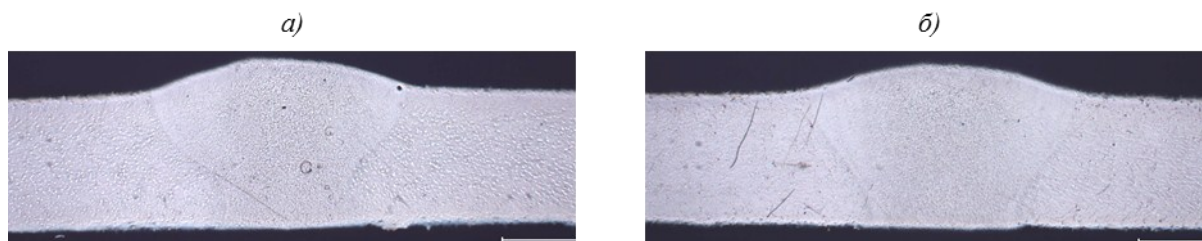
Макроструктура ( $\times 12,5$ ) сварных соединений сплава В-1579 на скорости сварки 0,04 (а) и 0,02 м/с (б)
